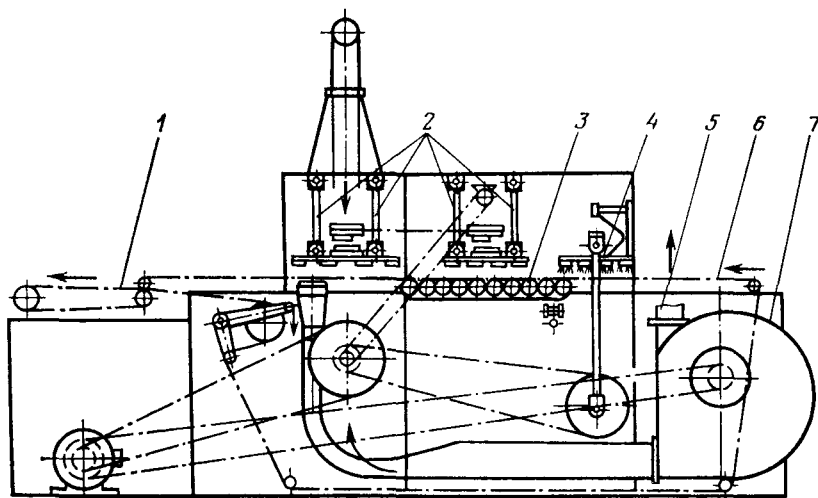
Машина для очистки корпусов конфет от крахмала
